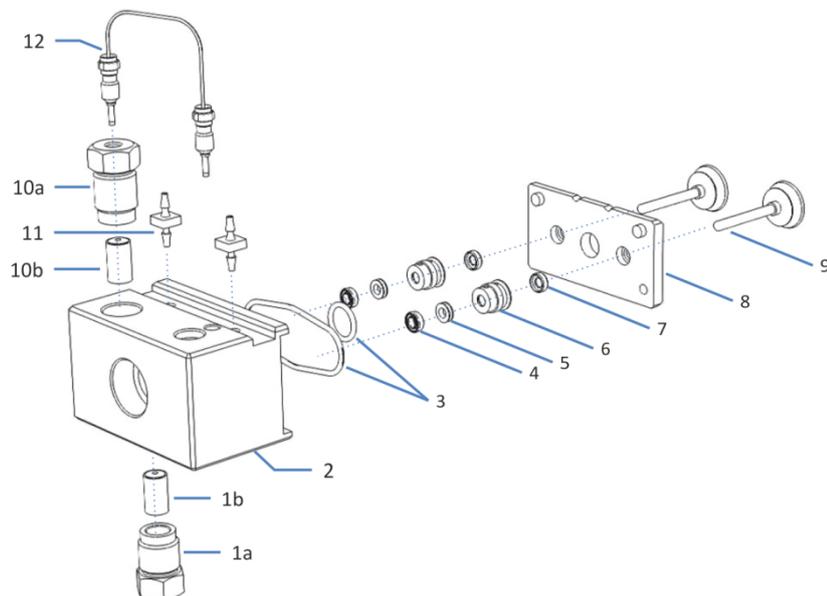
Vue d'ensemble des éléments de la tête de pompe
